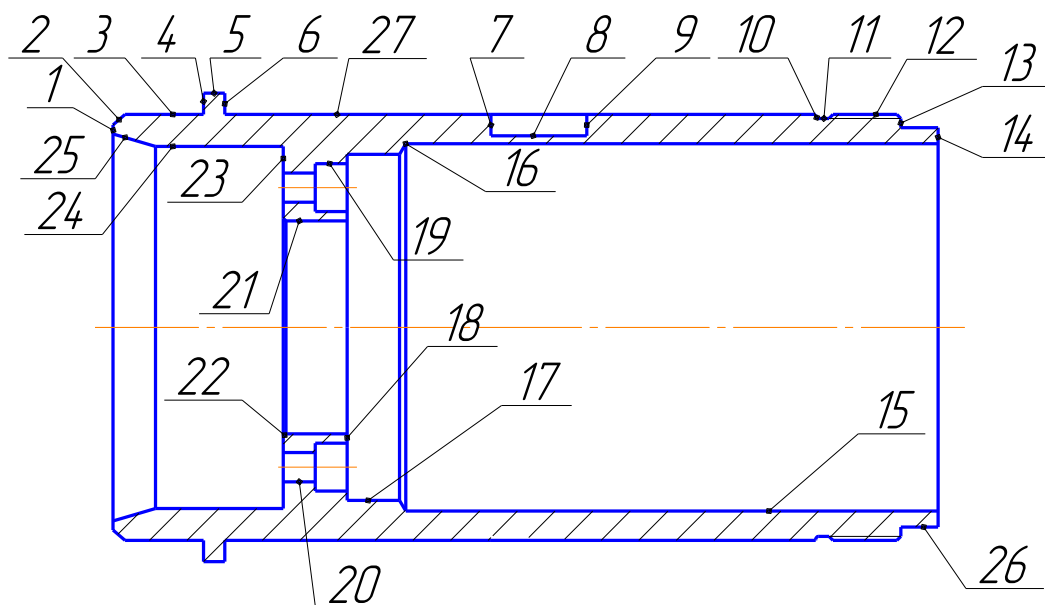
Ескіз класифікації поверхонь корпусу.
